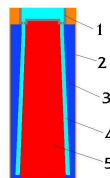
Отливка «Втулка коническая»: 1 – чаша из ПСС; 2 – воздух; 3 – кокиль; 4 – отливка; 5 – стержень из ПСС
